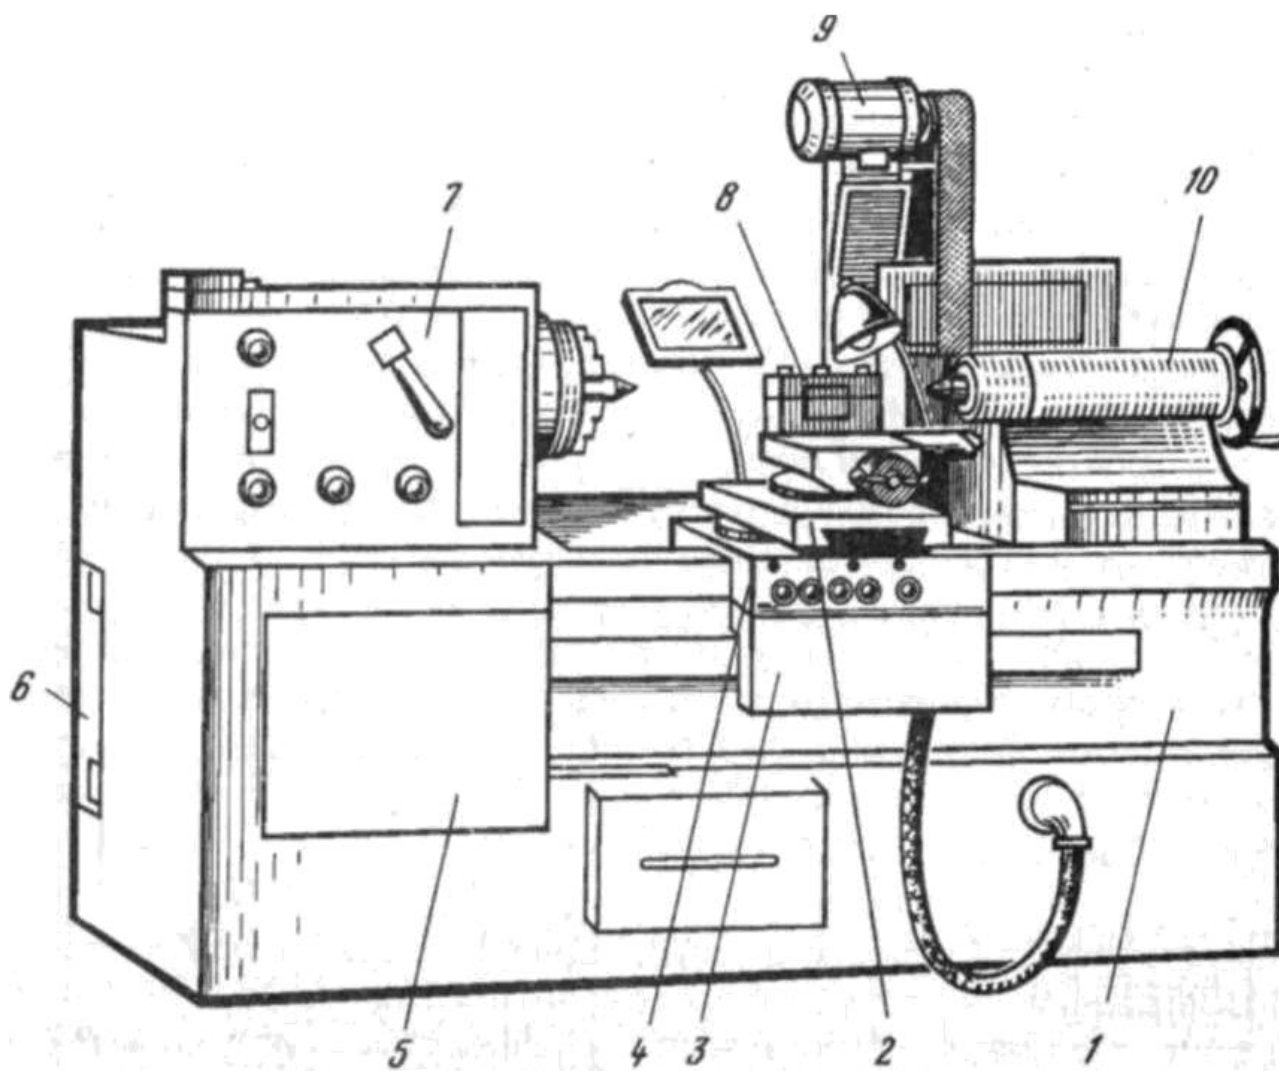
Универсальный токарно-затыловочный станок.
